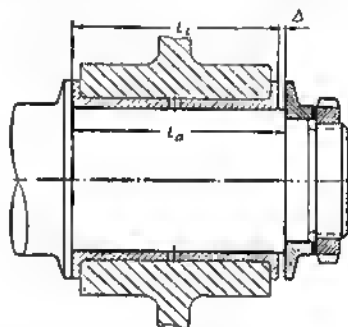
Esquema para determinar la holgura externa térmica en un cojinete de contacto plano de fijación
